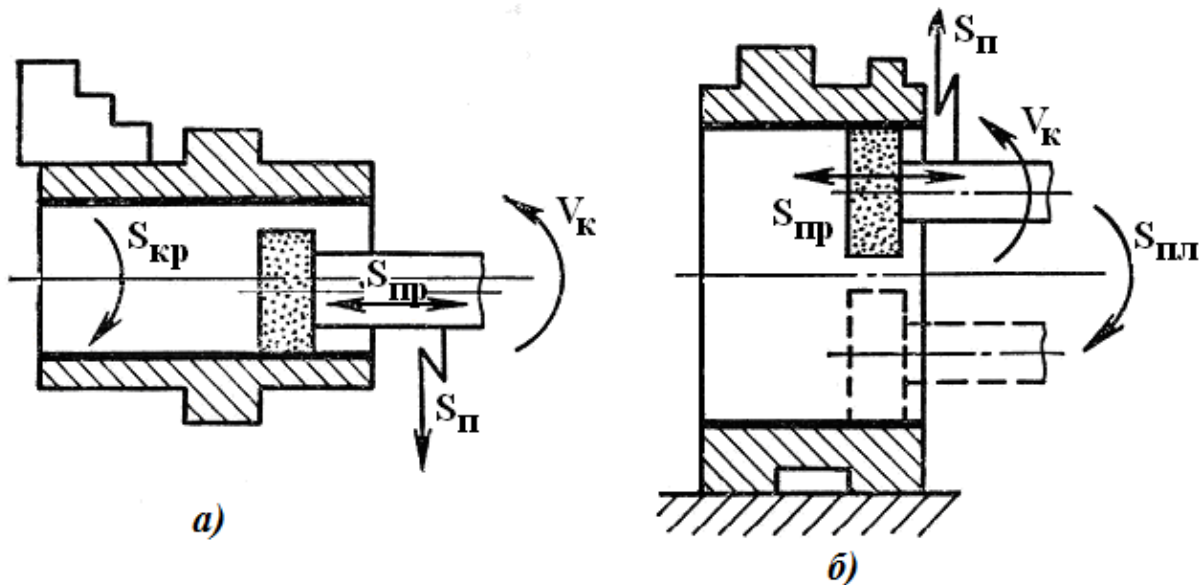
Схемы обработки заготовок на внутришлифовальных станках:
